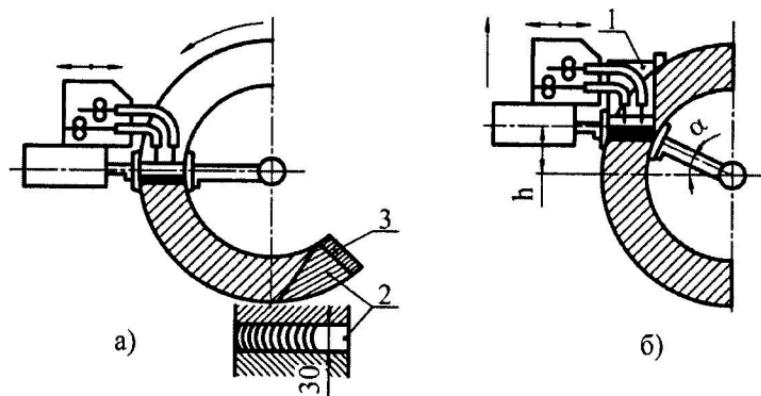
Схема електрошлакового зварювання кільцевого шва:
